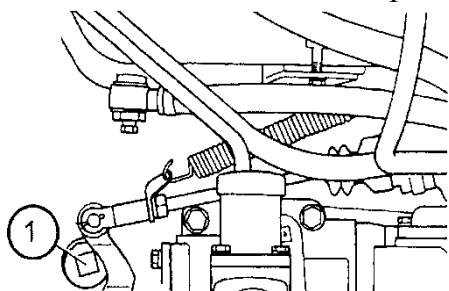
Смазка подшипника отводки сцепления: 1 – пробка
